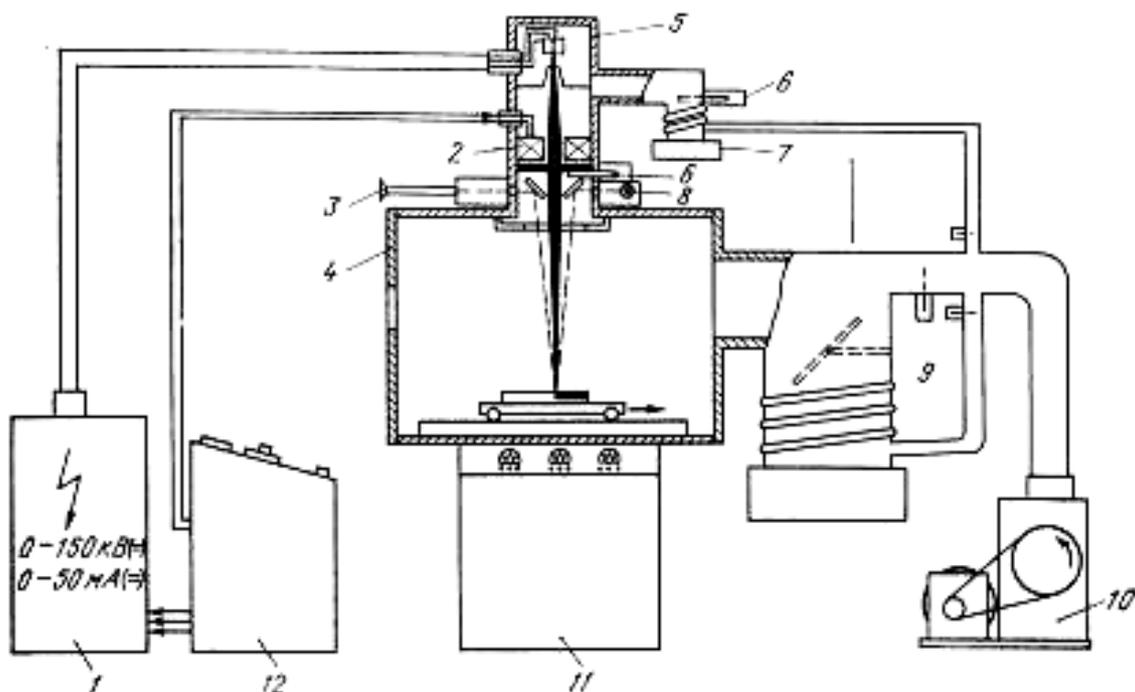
Принципиальная схема установки для электронно-лучевой сварки:
